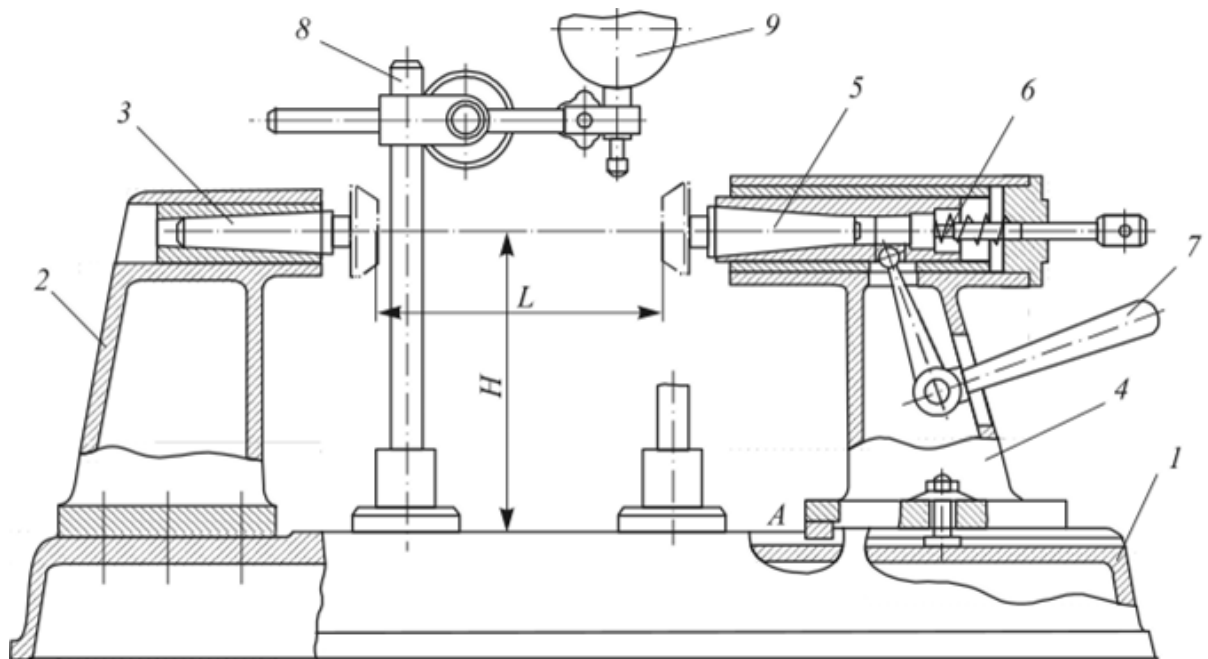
Універсальний пристрій з центрами для перевірки відхилення від співвісності циліндричних поверхонь тіл обертання
